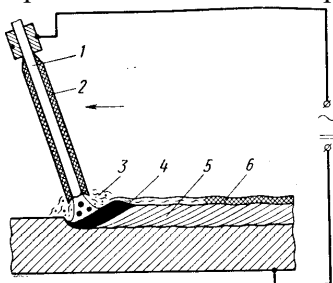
Схема поста для ручной дуговой сварки:
